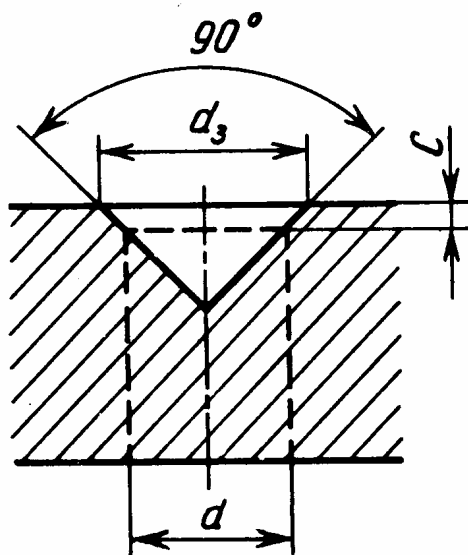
Схема центрування зі збереженням фаски після свердління
